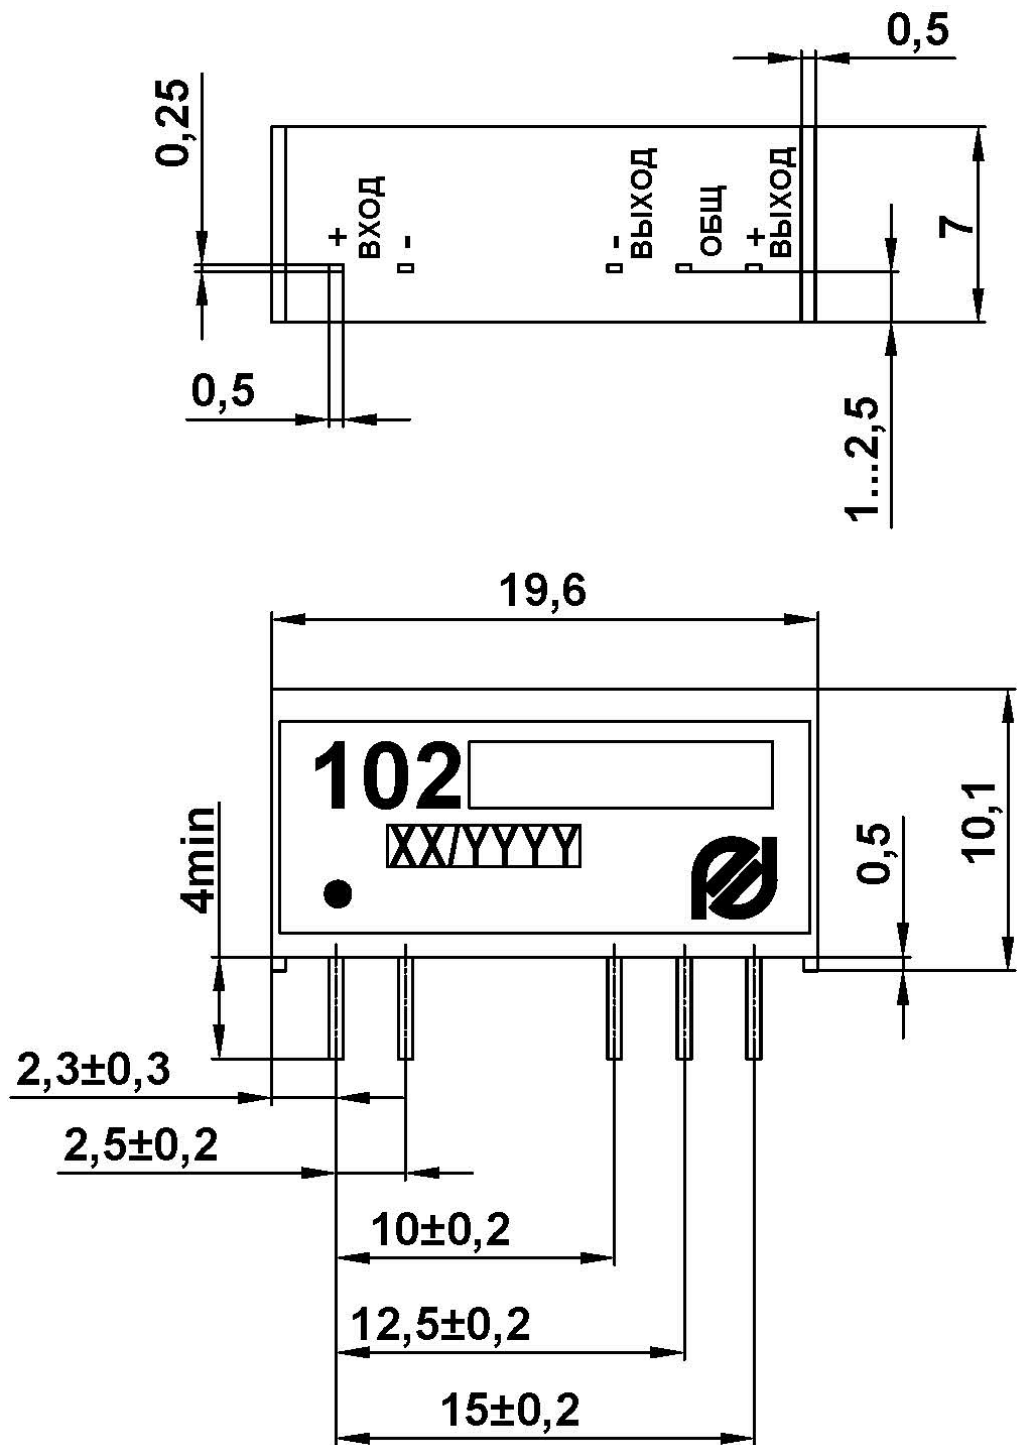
Габаритный чертеж одно- (двух) ваттных двухканальных модулей в конструктиве «В», корпусного исполнения
